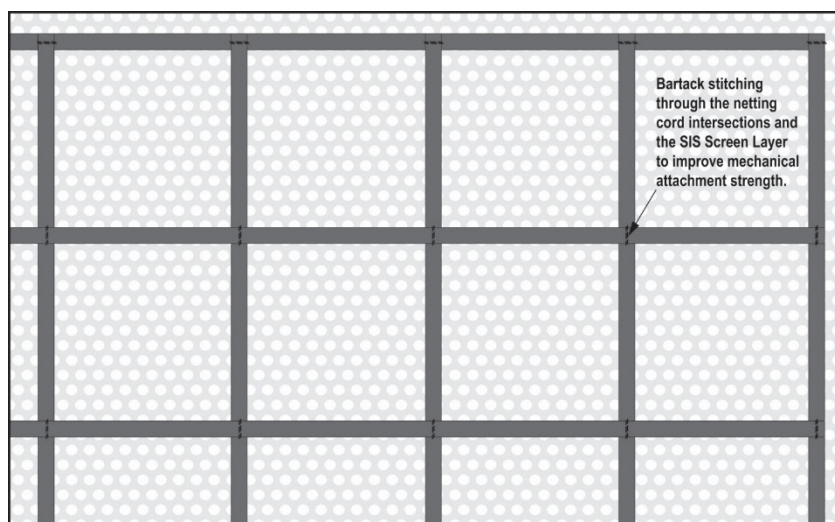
Gros plan du filet (dimensions du quadrillage 3 po x 3 po)
